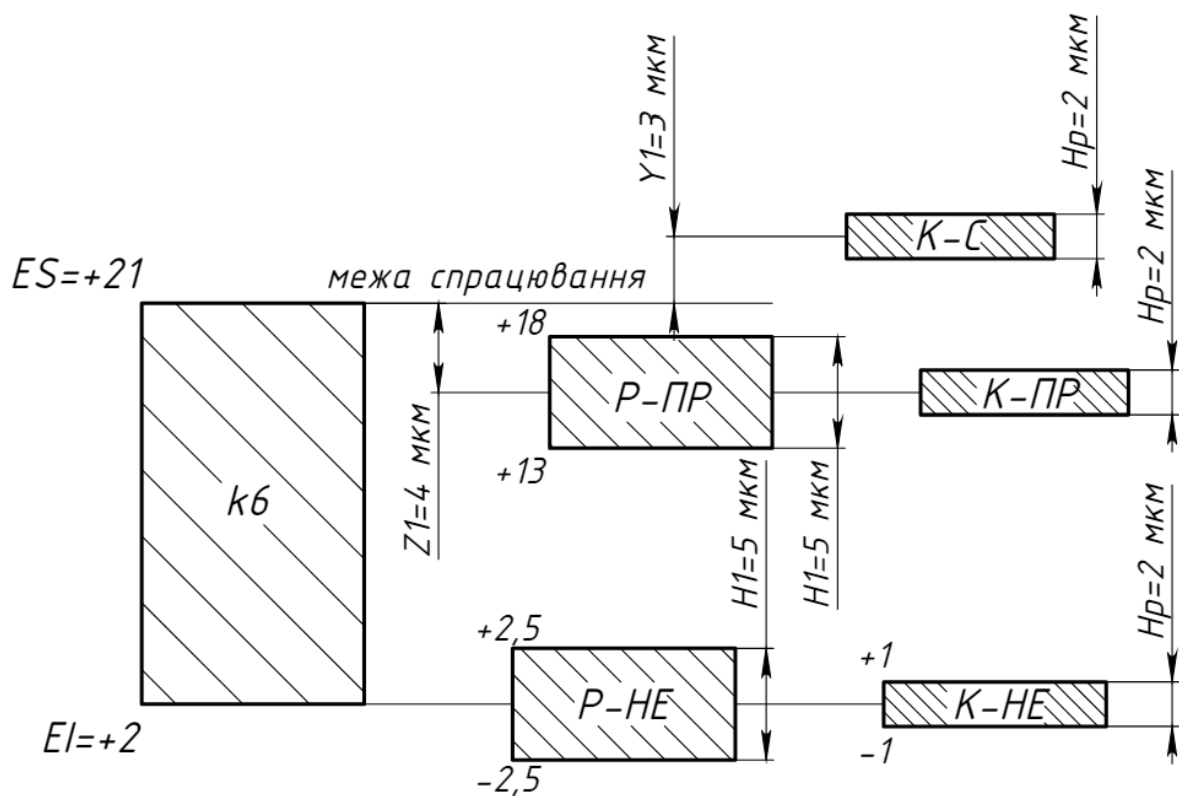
Схема розташування поля допуску для калібр-скоби
